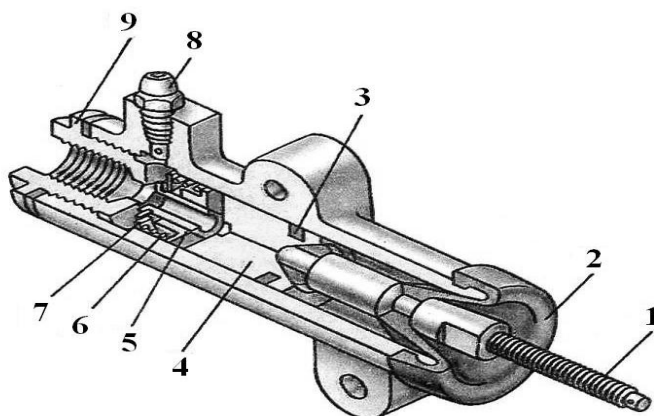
Рабочий цилиндр гидропривода выключения сцепления автомобилей ВАЗ:
